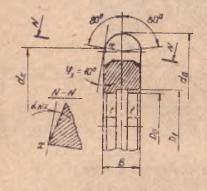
Задний угол в пормальном сечении для боковой точки режущей кромки
